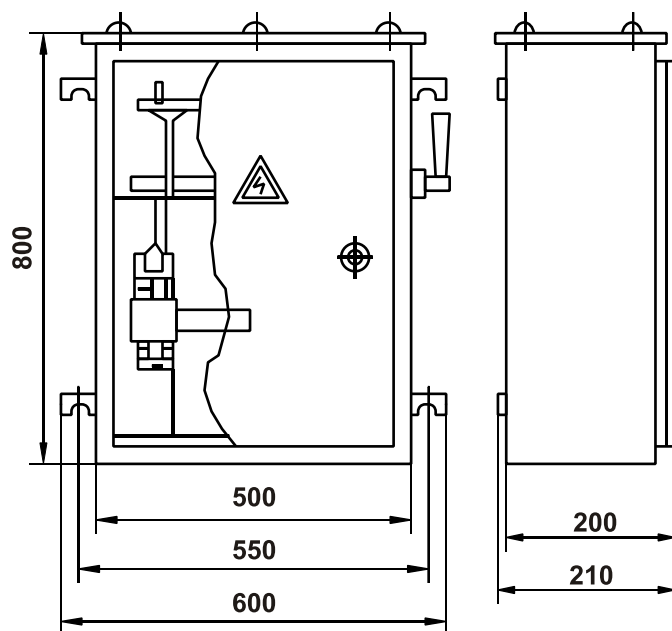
Внешний вид и габаритные размеры ЯВ
